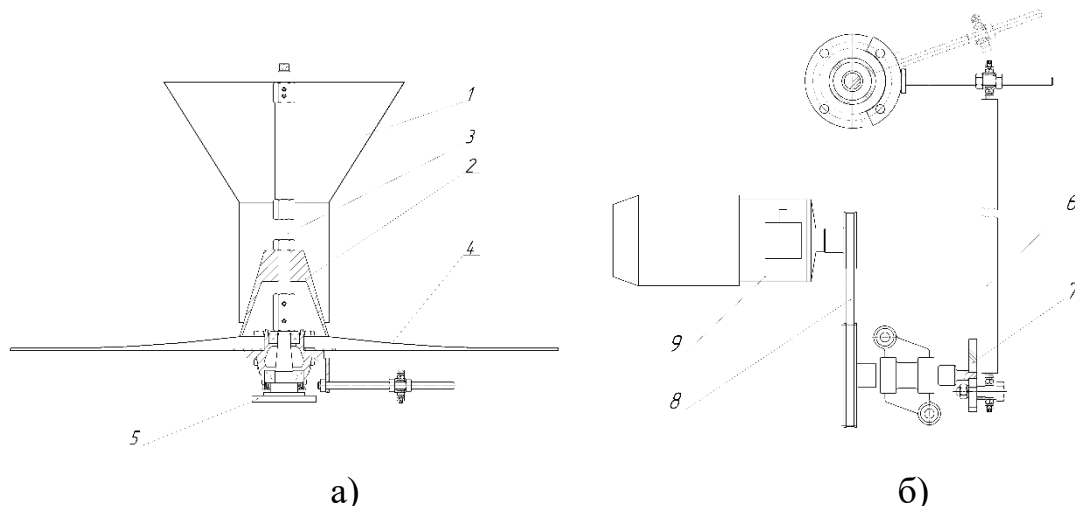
Схема робочої поверхні мікронізатора (а) та схема приводу мікронізатора (б): 1 – бункер; 2 – конус; 3 – вертикальна нерухома вісь; 4 – робоча поверхня; 5 – корпус з підшипниками; 6 – тяга; 7 – ексцентрик з наскрізним пазом; 8 – пасова передача; 9 – електродвигун.
